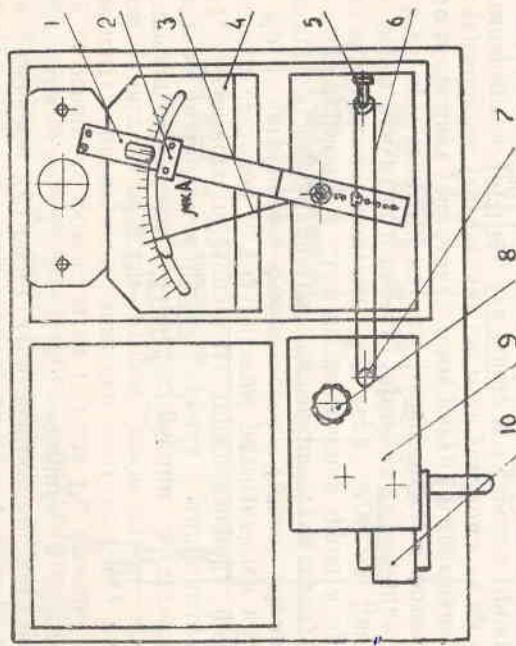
Кинематическая блок-схема регулирующего устройства: 1 — кронштейн; 2 — фотоэлемент ФСК-1; 3 — стрелка миллиамперметра; 4 — миллиамперметр; 5 — натяжной блок; 6 — стальная струна; 7 — приводной барабан; 8 — штурвал; 9 — ручная настройка; 10 — электродвигатель ДС-2.
